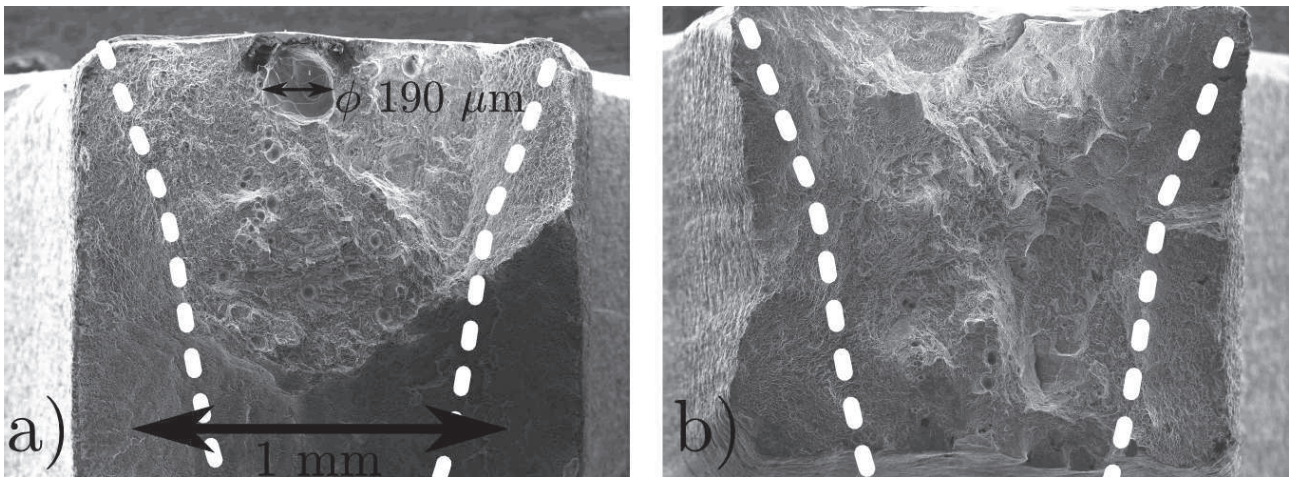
Faciès de rupture observés au microscope électronique à balayage, a) éprouvette soudure *longitudinale 3* et b) éprouvette soudure *longitudinale 6
